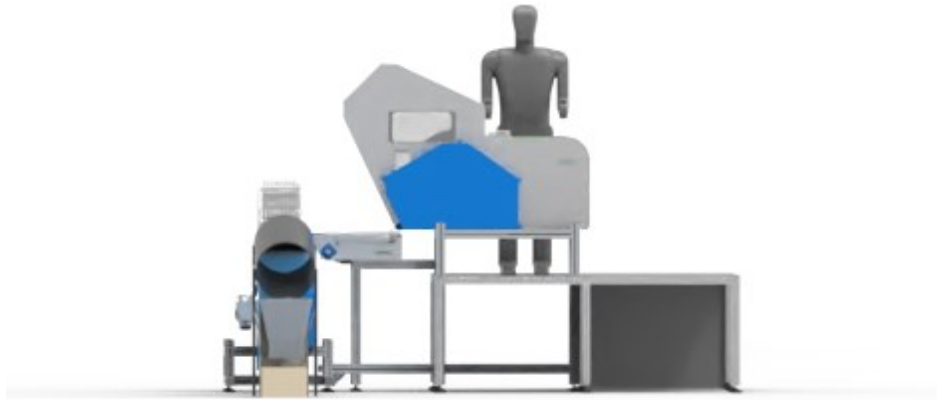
Layout complessivo del blocco 1 (vista frontale)
